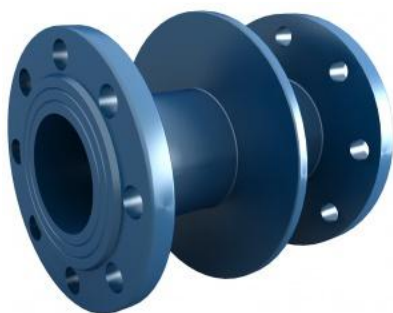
Общий вид приемо-раздаточного патрубка [56]
